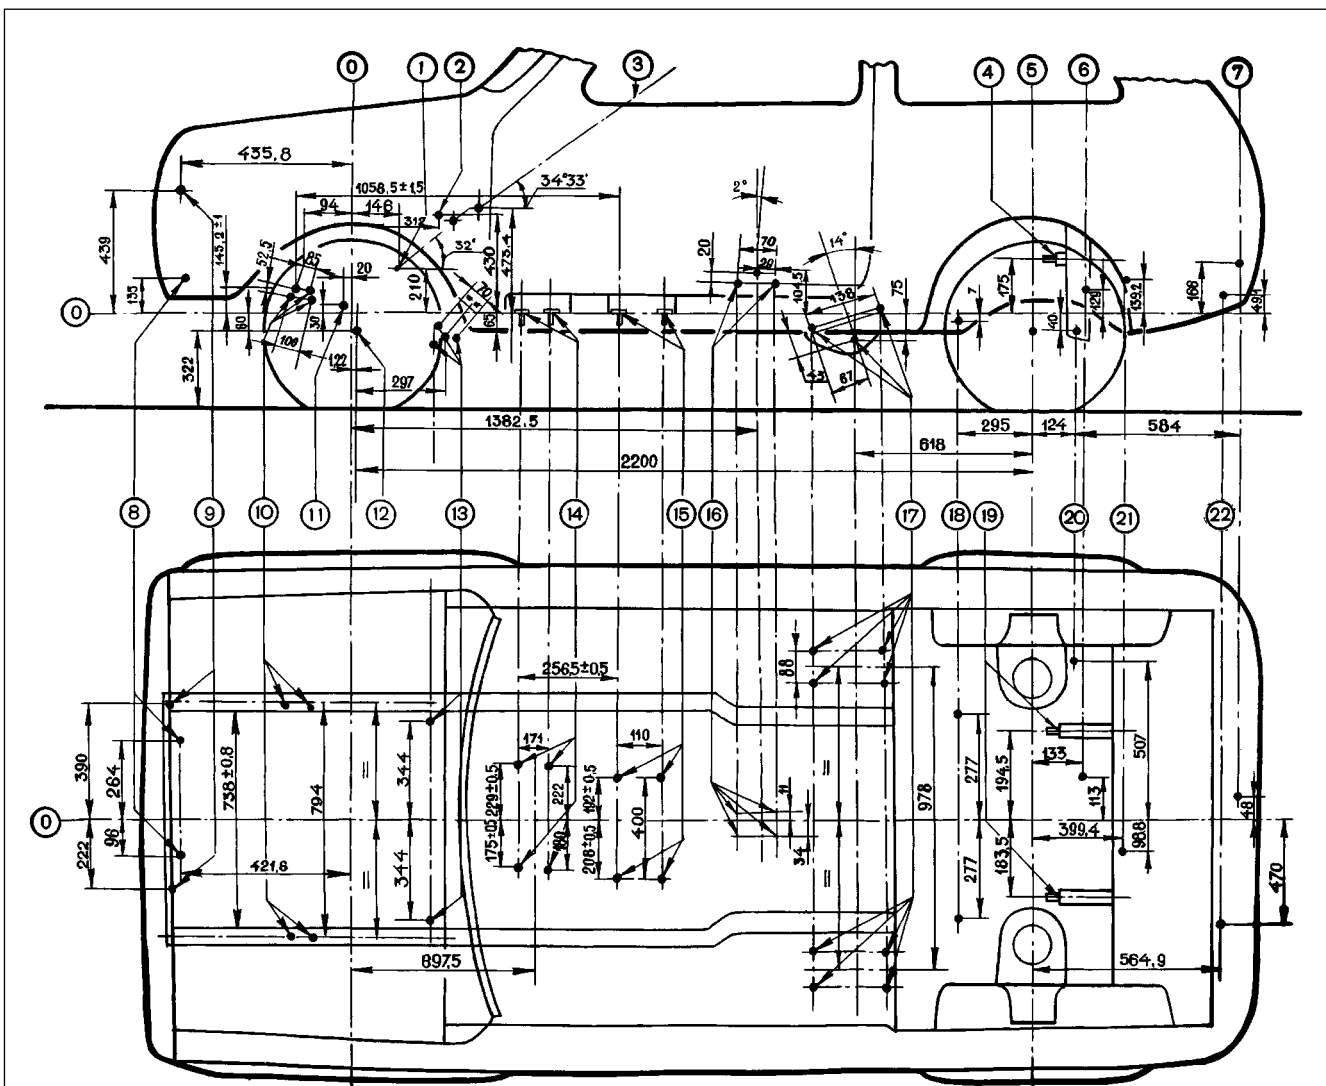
Befestigungspunkte von Baugruppen und Aggregaten des Fahrzeuges:
